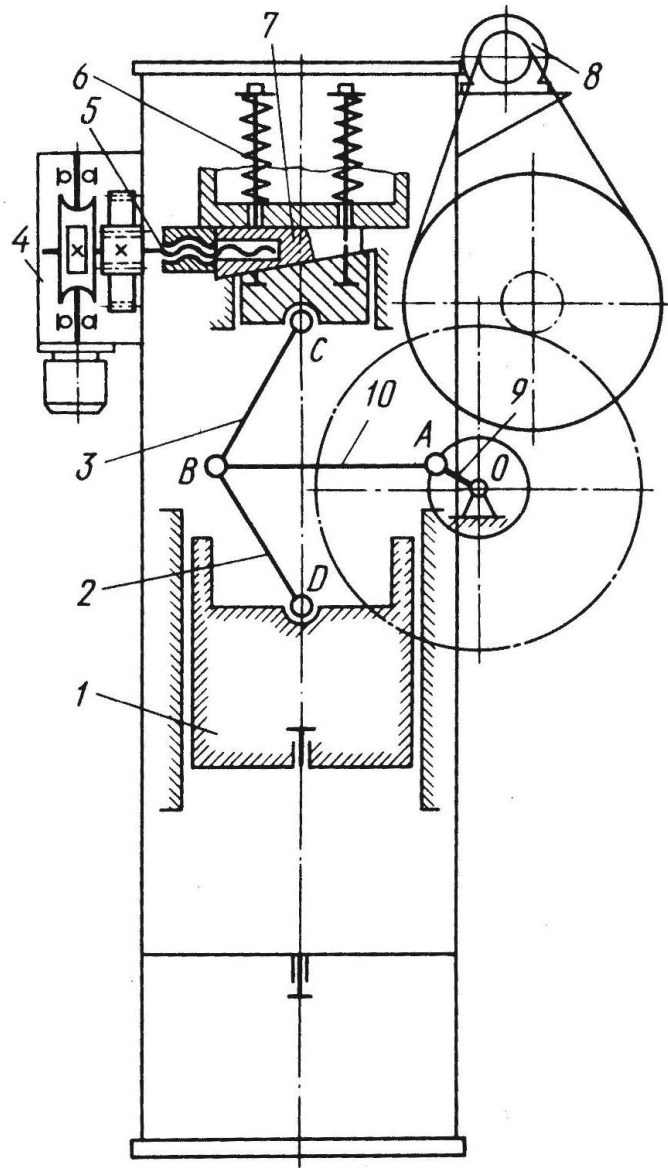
Исполнительный механизм кривошипно-коленного пресса
